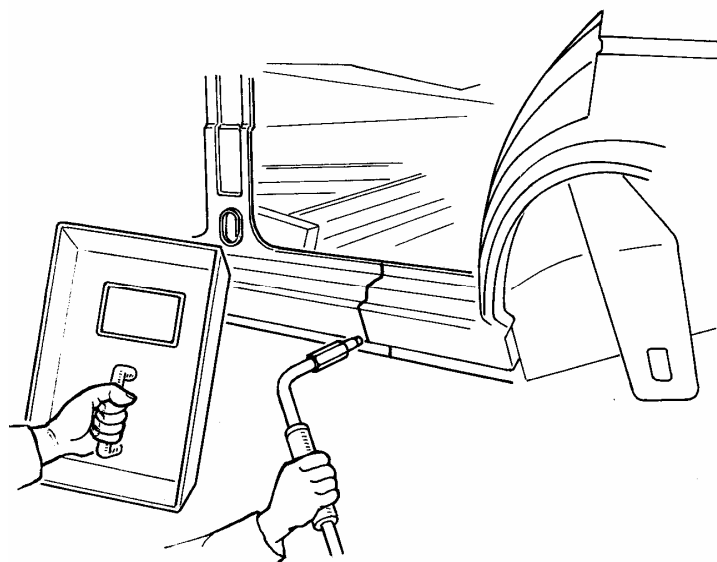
Acople de la pieza nueva y soldadura.
